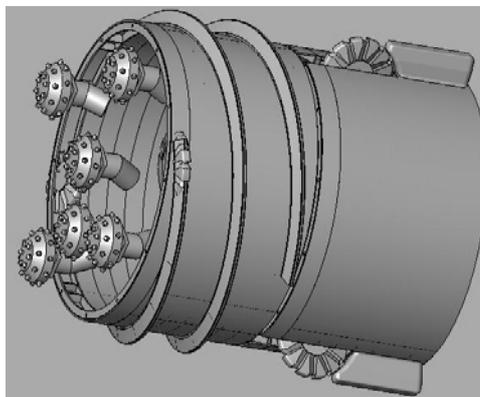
Расположение поворотной секции перед неповоротной с использованием промежуточного звена редуктора привода вращения движителя для размещения агрегата
